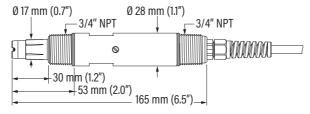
H17640-18zz sonda galvânica de OD com cabo acoplado
